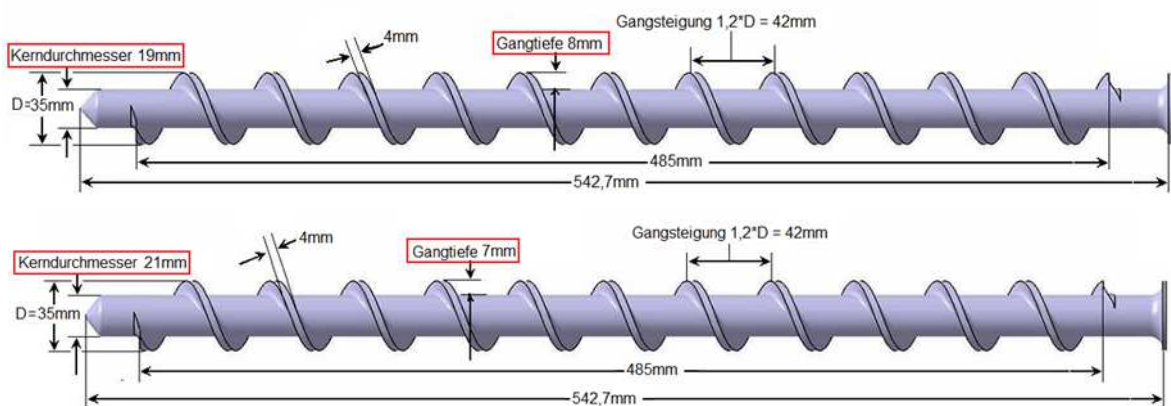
Schneckenvarianten A und B mit geänderter Gangtiefe
